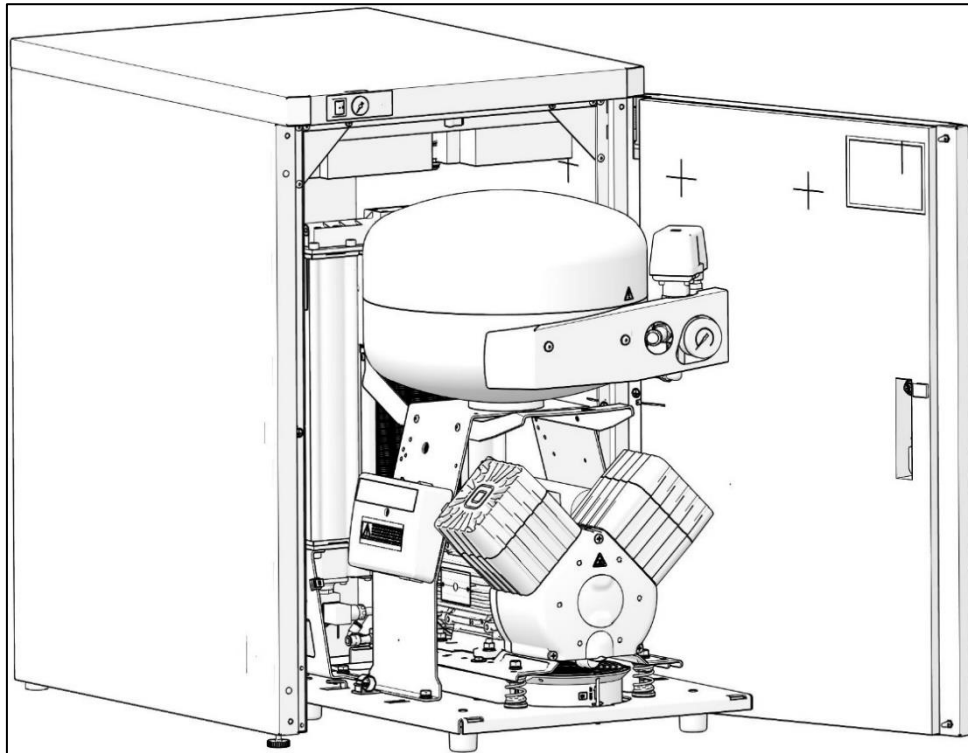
Positionierung des Kompressors für elektrische Anschlüsse
